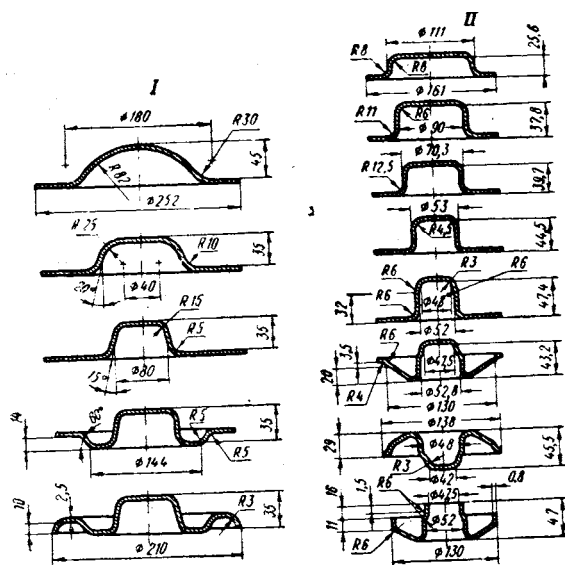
Примеры (I-II) построения технологических переходов штамповки при изготовлении деталей сложной формы прямой и реверсивной вытяжкой
